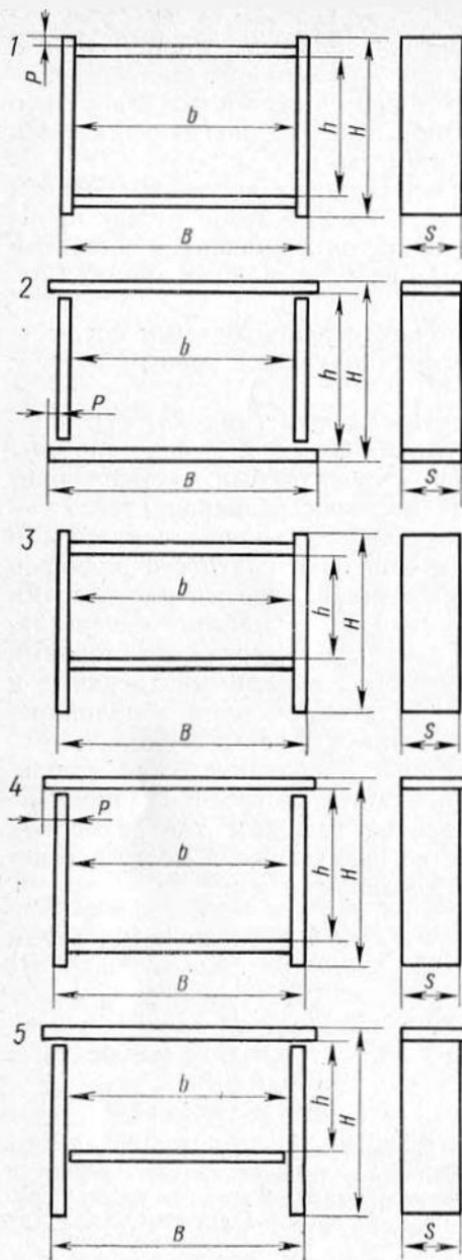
Схемы сборки корпуса изделий в ОСУ-81:
